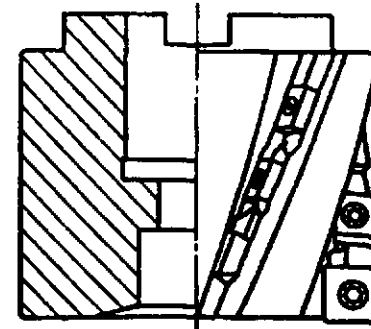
Торцовая насадная фреза с квадратными пластинами, чередующимися от зуба к зубу в шахматном порядке
